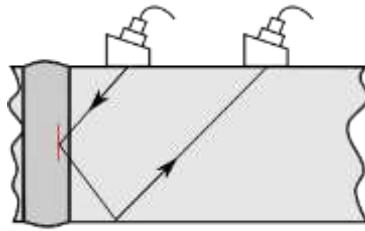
Схема ультразвукового контролю зварного з'єднання
